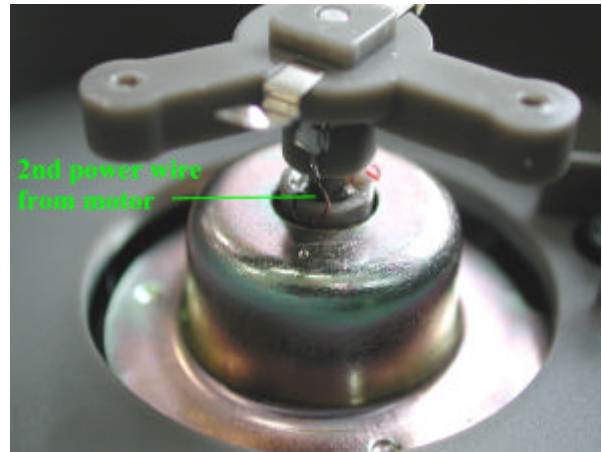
Flansch mit zwei Kontaktfedern zur Betriebsspannungsversorgung des Boards
